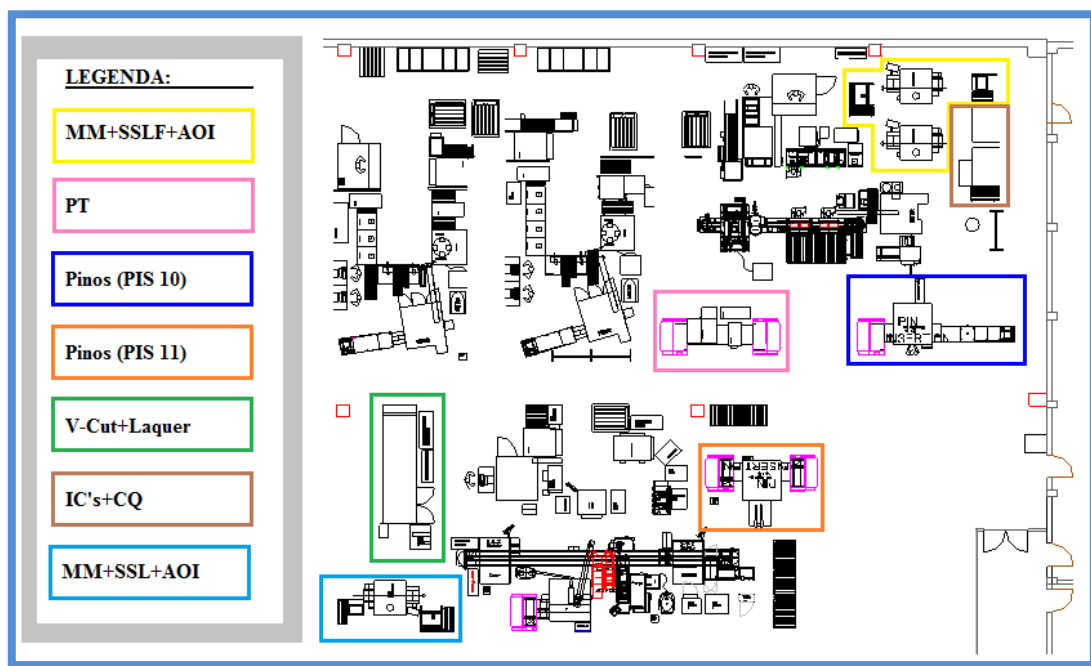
Layout da secção (identificação dos subprocessos da pré-montagem)
